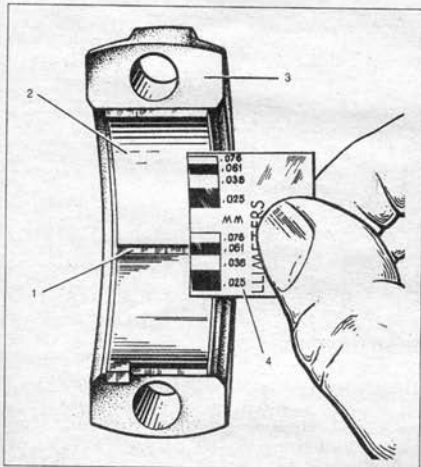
Измерение зазора в шатунном подшипнике: 1 - сплюснутая калиброванная пластмассовая проволока; 2 - вкладыш; 3 - крышка шатуна; 4 - шкала для измерения зазора
